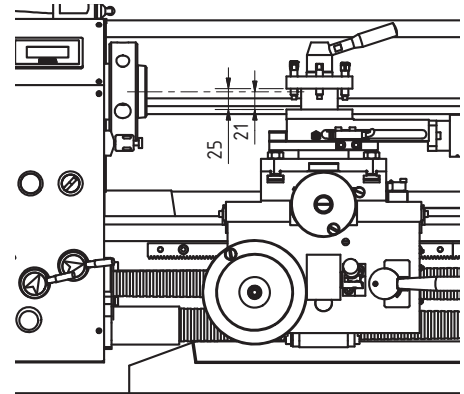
Hauteur jusqu'au centre de rotation 21 mm
